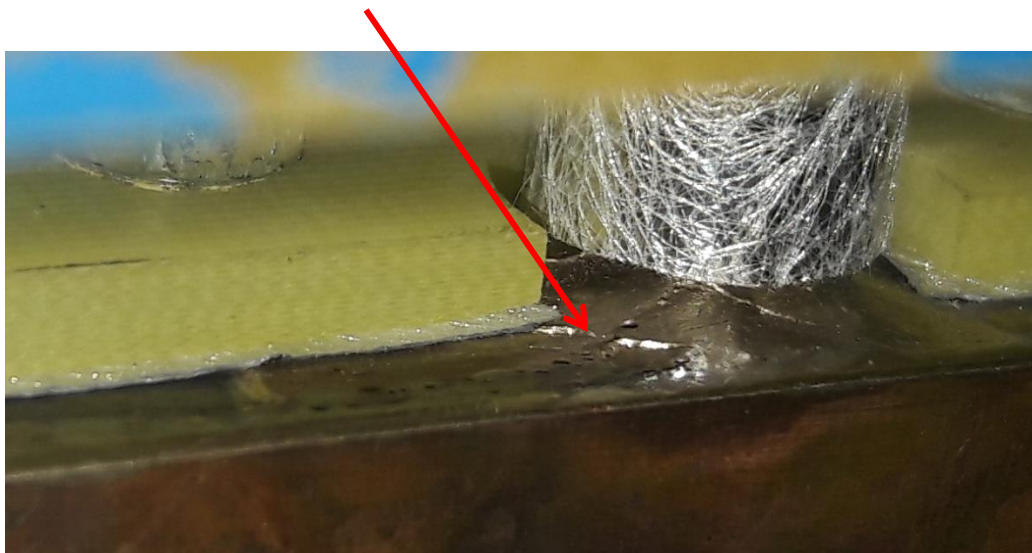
Zoom das trincas na solda lado esquerdo
